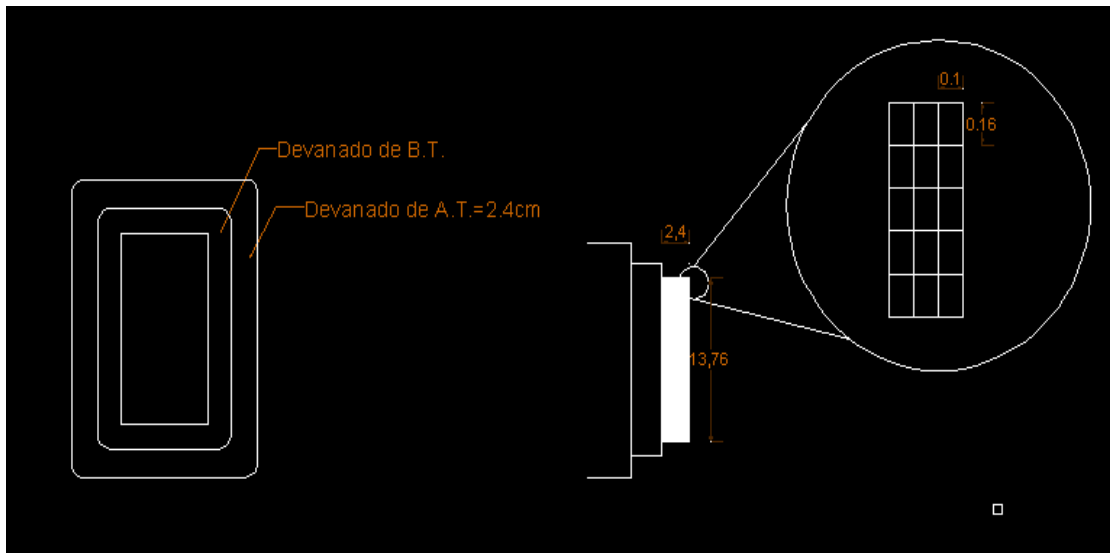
Dimensiones calculadas del devanado de alta tensión.
